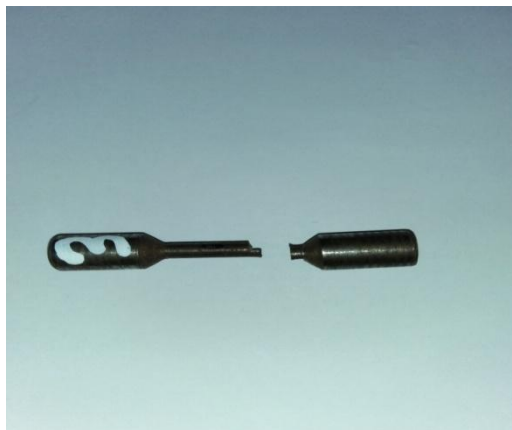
Spesimen 2 baja st 60 dengan beban 20 kg.
